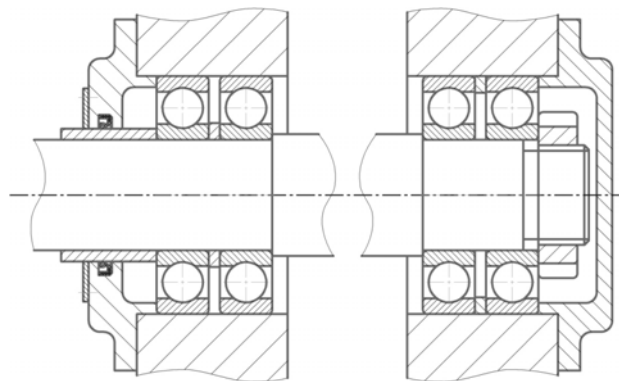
Вал с 4-мя подшипниками в корпусе
